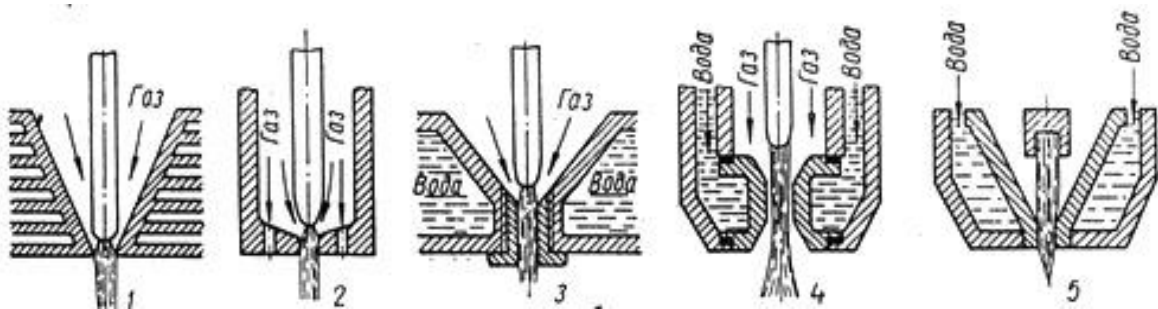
Основні конструкції плазмотворюючих сопел [89].
